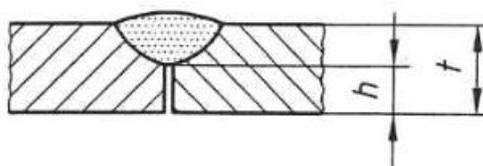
Soldadura com penetração incompleta na raiz
